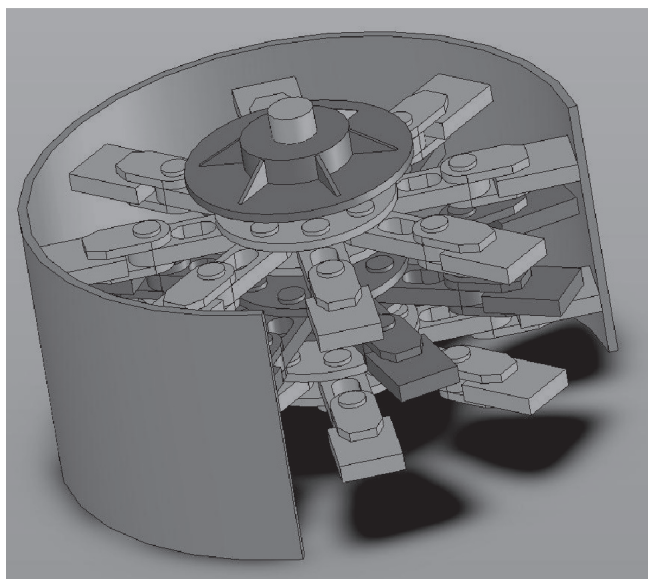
Принципиальная конструкция молотковой дробилки с вертикальным ротором: 1 — вал; 2 — диск; 3 — серьга; 4 — било; 5 — подшипниковая опора; 6 — подвижные шарниры (пальцы); 7 — корпус
